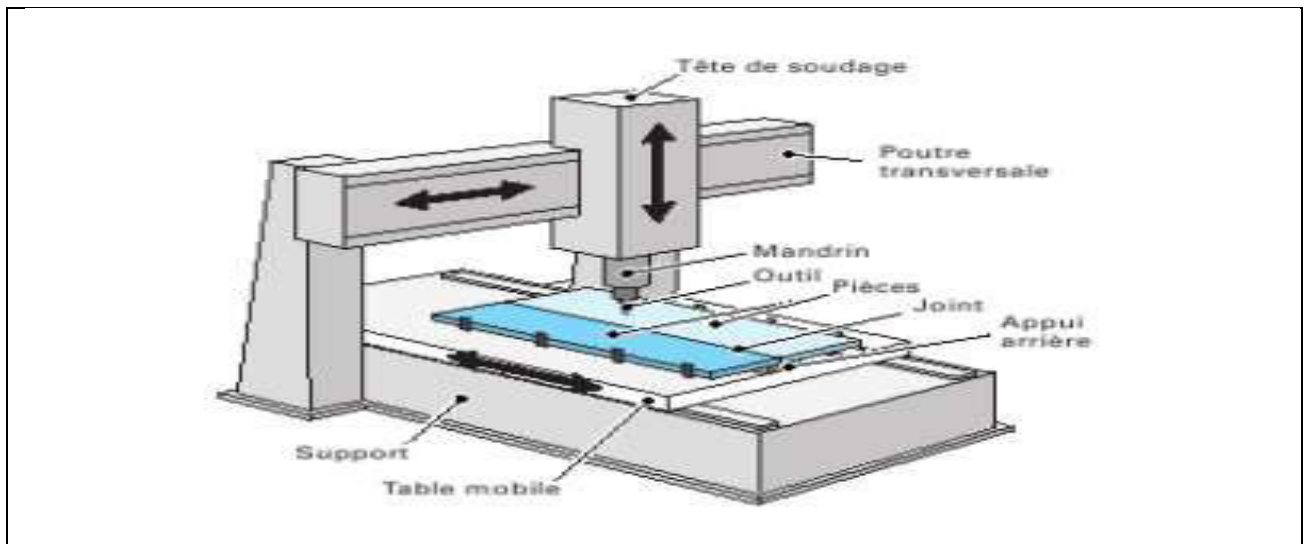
Schéma d'une machine-outil pour le FSW [15] [21]
